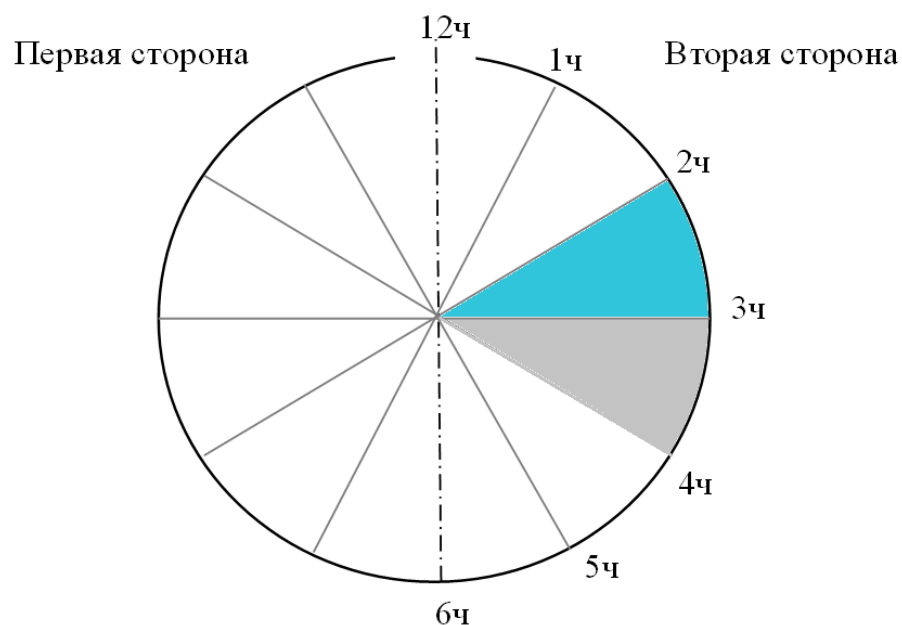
Области трубной заготовки после шаговой формовки
